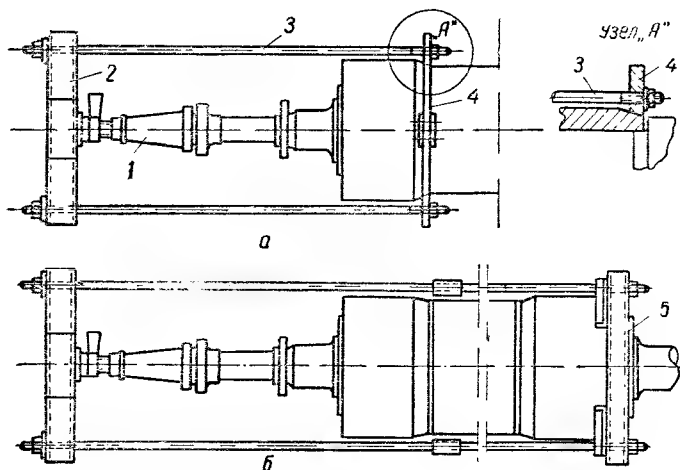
Приспособление для съема и насадки массивных бандажей: а — положение приспособления при съеме бандажа; б — положение приспособления при насадке бандажа; 1 — домкрат; 2 — упорная крестовина; 3 — тяги; 4 — разъемное кольцо для захвата бандажа при съеме; 5 — рама для захвата бандажа при насадке.
